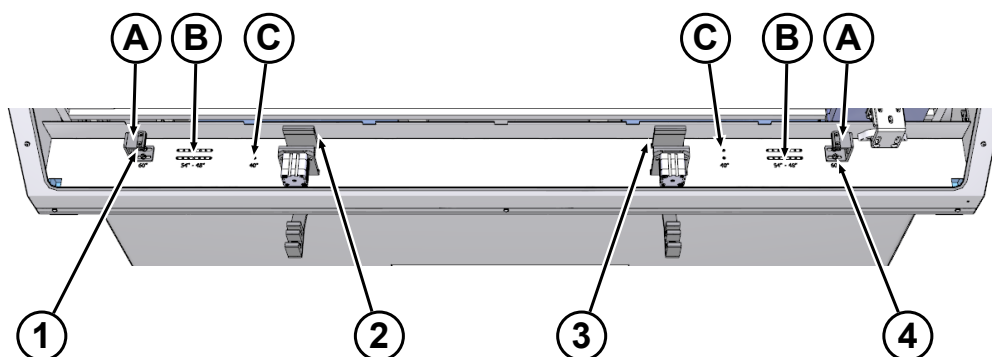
Possíveis posições dos suportes do chapéu de cardagem na área de ruptura
